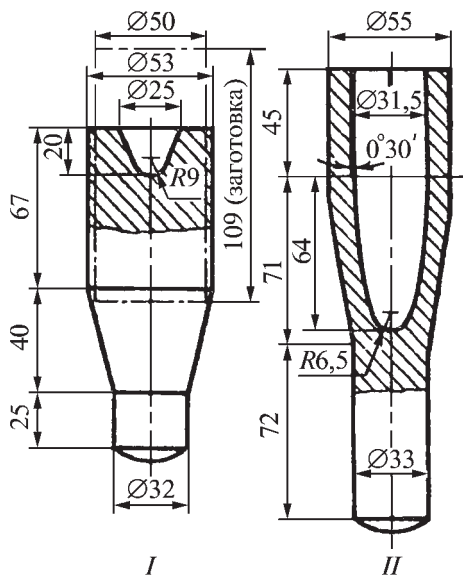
Двухпереходная штамповка поковки с глухой полостью:
